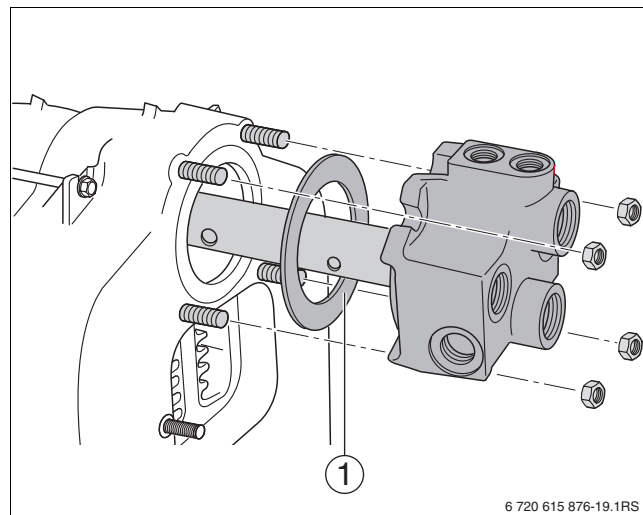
Montage du tube injecteur et de la pièce de raccordement spécifique
